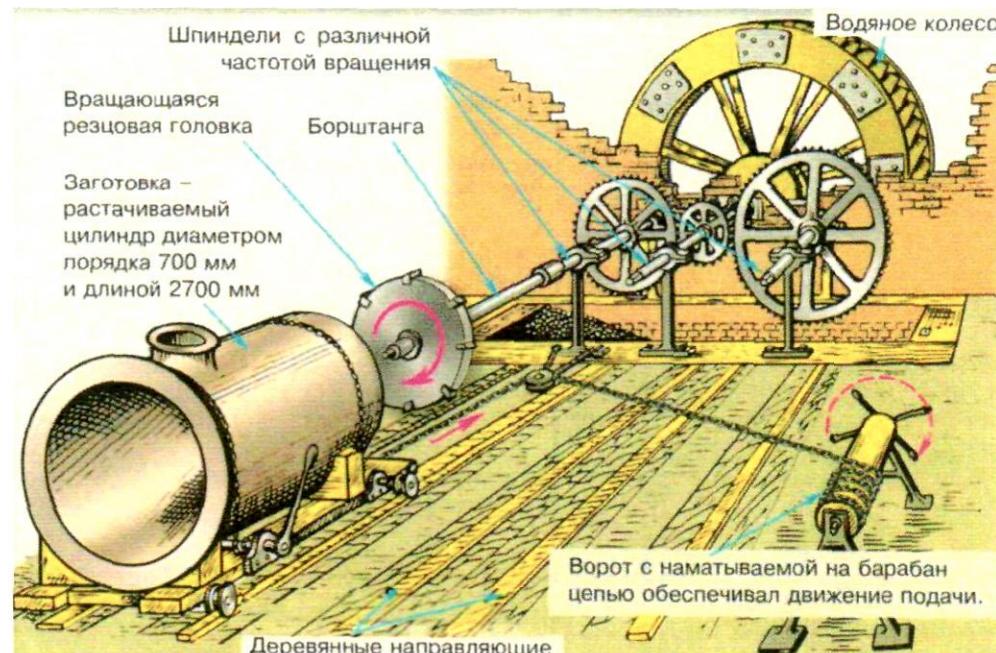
Станок Д. Смитона для обработки внутренней поверхности цилиндра
